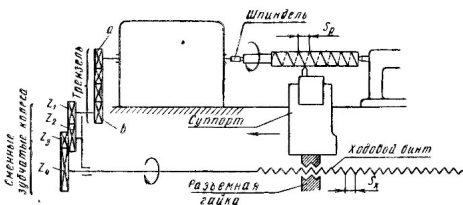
Схема передачи движения от шпинделя к ходовому винту при нарезании резьбы на токарно-винторезном станке
